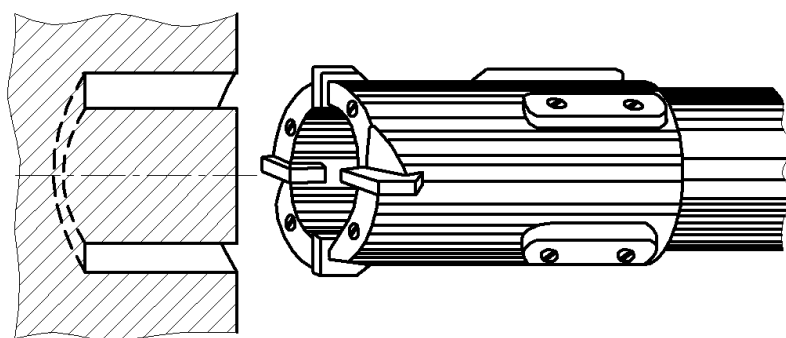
Схема оброблення свердлом для кільцевого свердління
